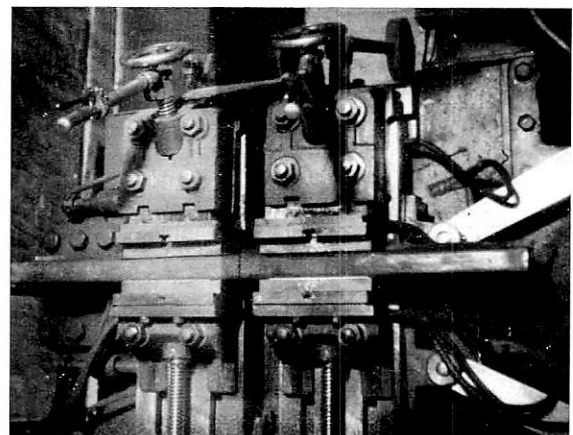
Schienenstücke in der Maschine eingespannt. Fertig zum Schweißen.
